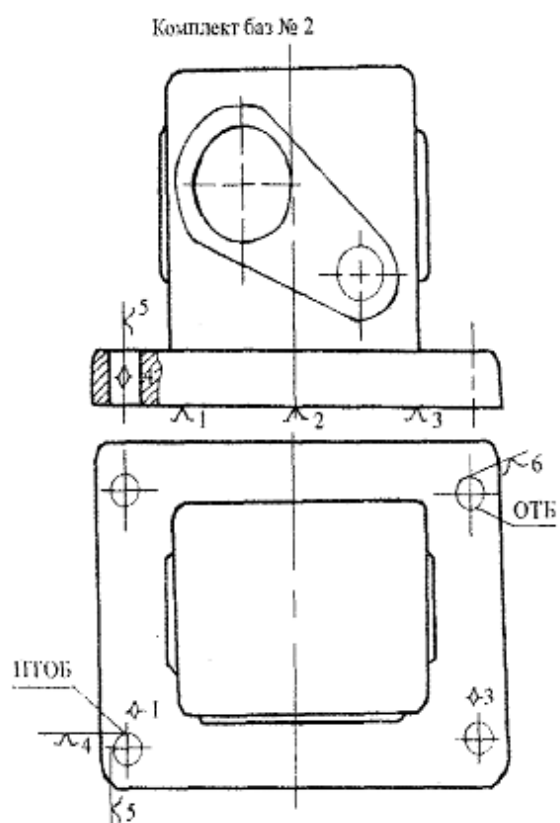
Теоретична схема базування корпусної деталі на площину і два отвори
